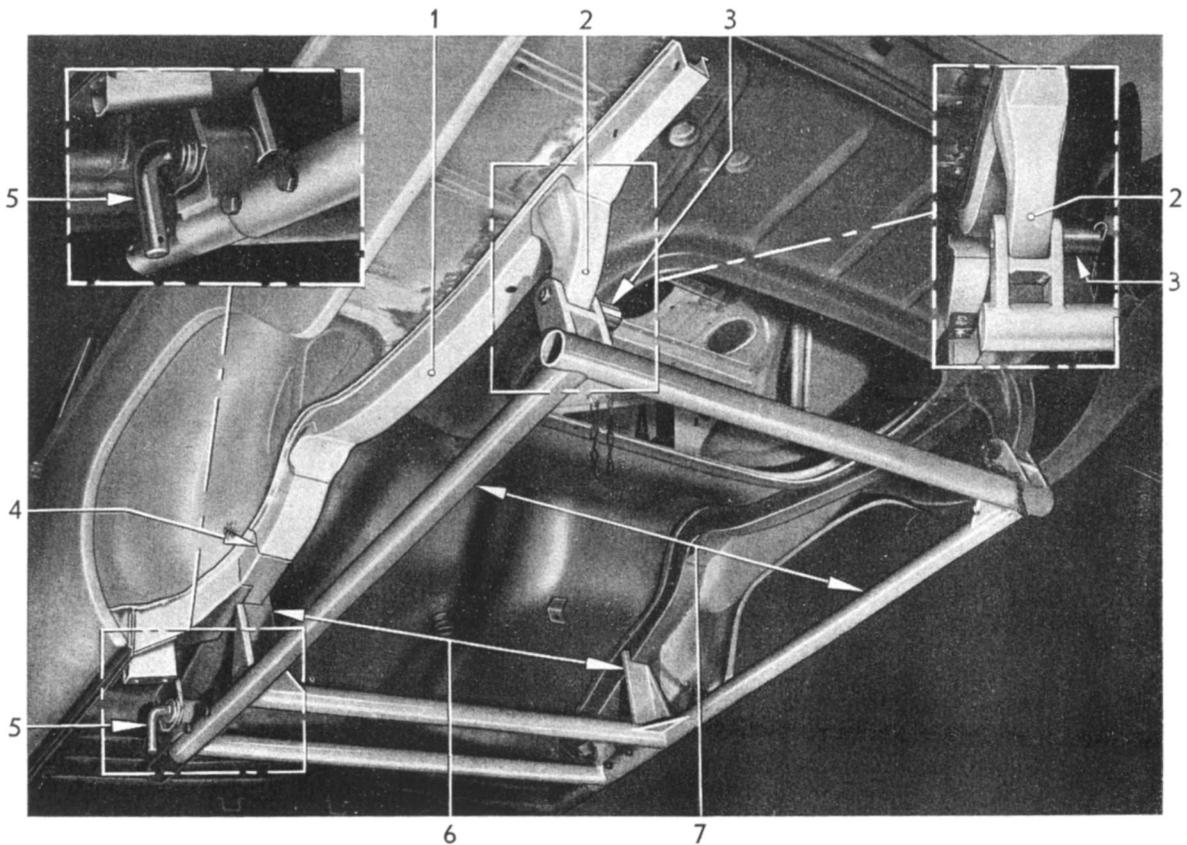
Neues Längsträgerhinterteil mit Hinterlängsträger-Schweißblehre S-1151 ausgerichtet
